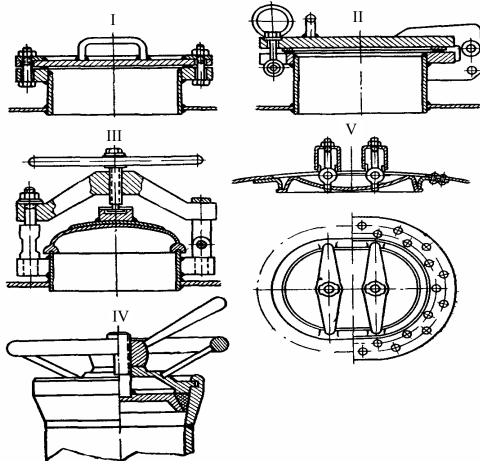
Люки и лазы: I – люк с глухими болтами; II – люк с откидными болтами; III – люк со скобой; IV – люк с байонетным затвором; V – овальный люк
